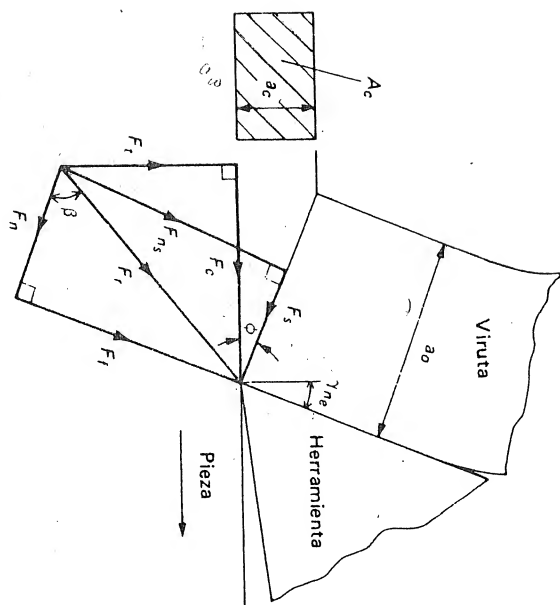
Diagrama de fuerzas para el corte ortogonal, donde F_r = fuerza resultante sobre la herramienta, F_c = fuerza de corte, F_t = fuerza de empuje, F_s = fuerza de cizalladura sobre el plano de cizalladura, F_{ns} = fuerza normal sobre la cara de la herramienta, F_{ti} = fuerza de fricción sobre la cara de la herramienta, F_{ni} = fuerza normal sobre la cara de la herramienta, ϕ = ángulo de cizalladura, γ = ángulo de inclinación efectiva, β = ángulo medio de fricción sobre la cara de la herramienta, A_c = área de la sección de la viruta sin cortar, a_c = espesor de la viruta no deformada, y a_0 = espesor de la viruta.
